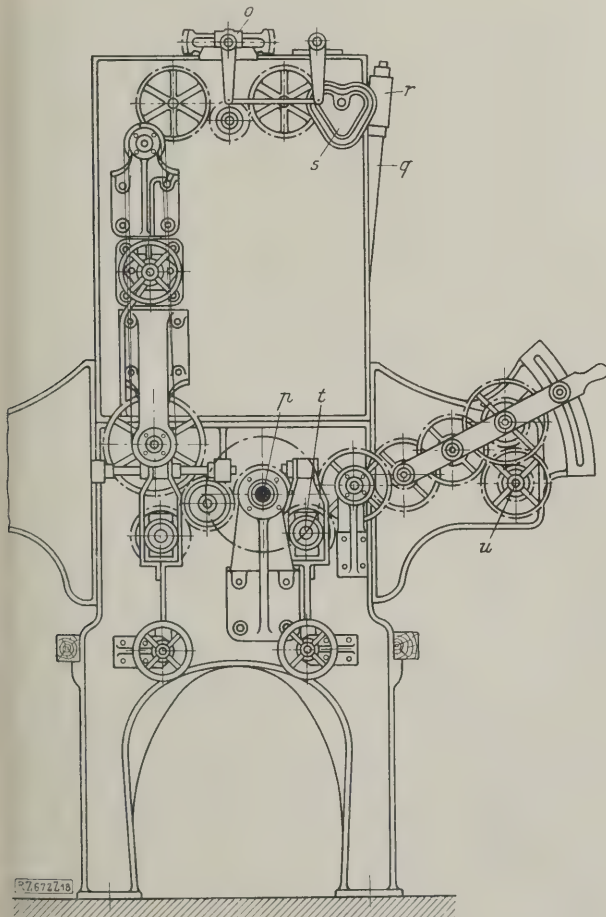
und 19. Stirnansicht und Querschnitt einer Zentrifugen-Spinnmaschine mit Schneckenradantrieb.
